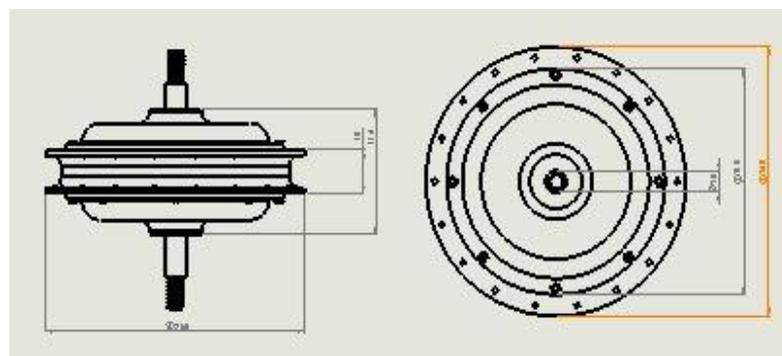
(a) Cover samping BLDC, (b) Ass stator
